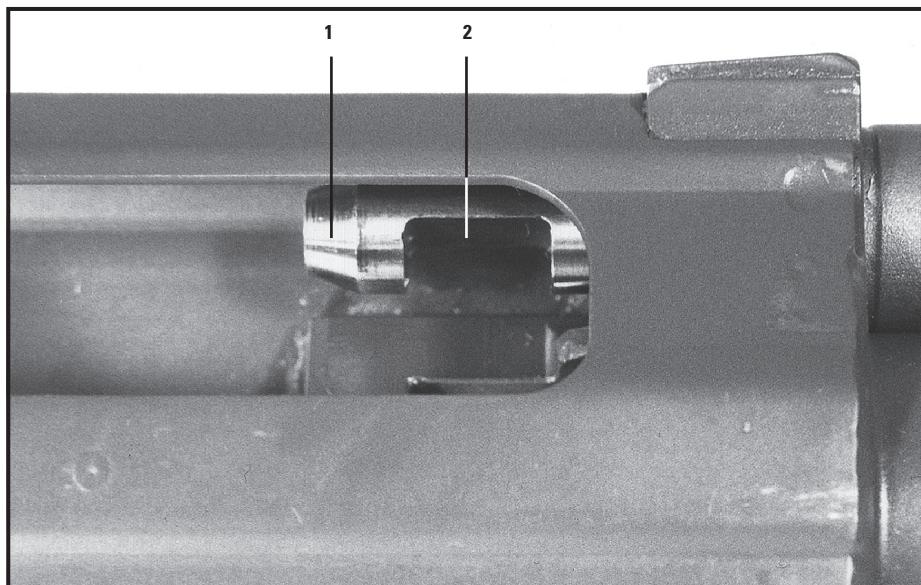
Montaggio dell'asta d'armamento: posizione corretta della tacca di bloccaggio
